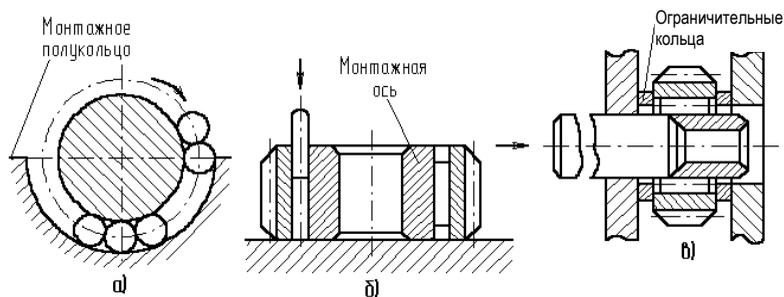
Сборка сборочных единиц с игольчатыми подшипниками
